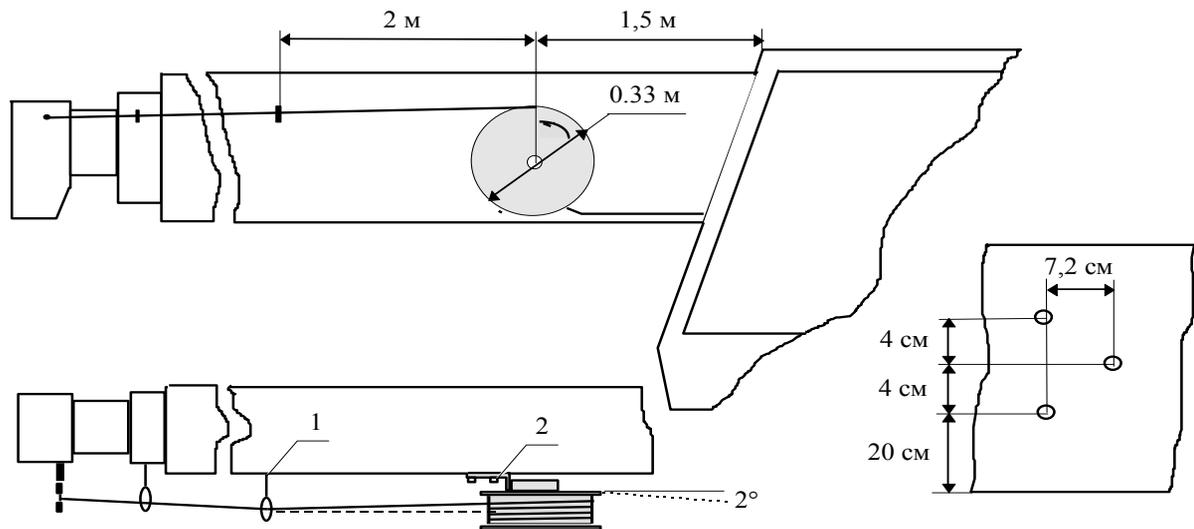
Установка датчика длины и разметка мест его крепления
